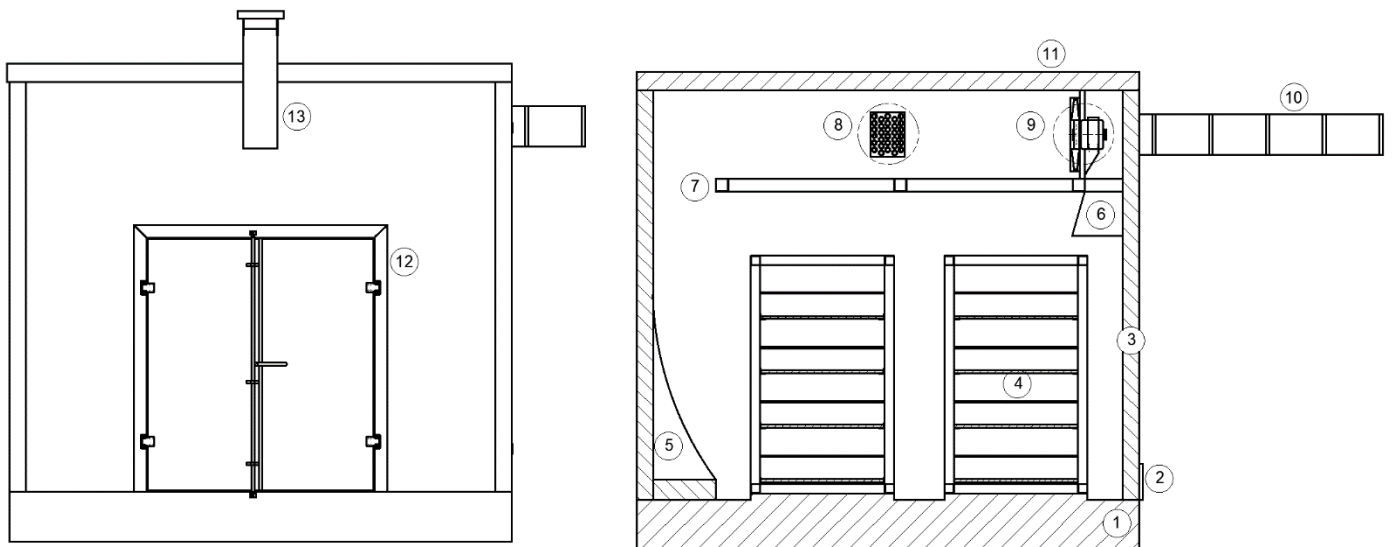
Izquierda: Vista frontal horno - Derecha Corte de Cámara de secado. Fuente: Autor.
